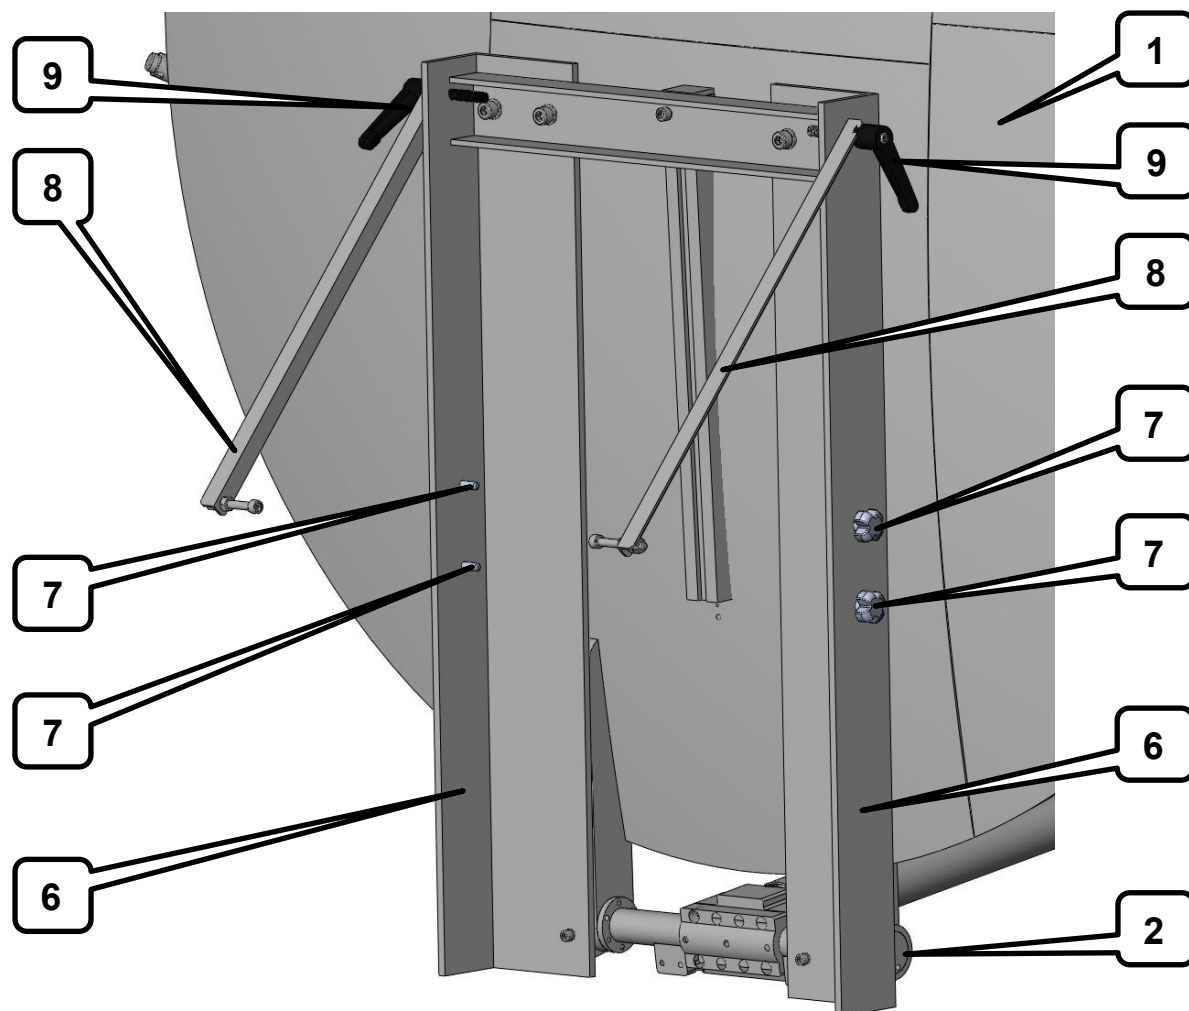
Внешний вид кронштейна рефлектора в сборе
